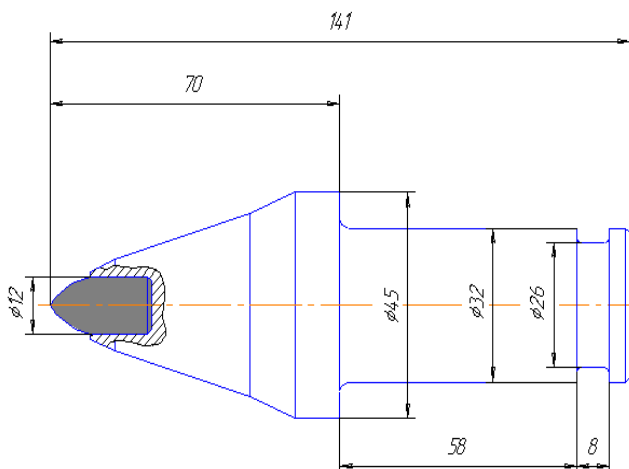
Тангенциальный поворотный резец РШ 32-70/16 ВЛ с цилиндрической твердосплавной вставкой фирмы Boart Longyear Stiff D12,0x23 BF T6
